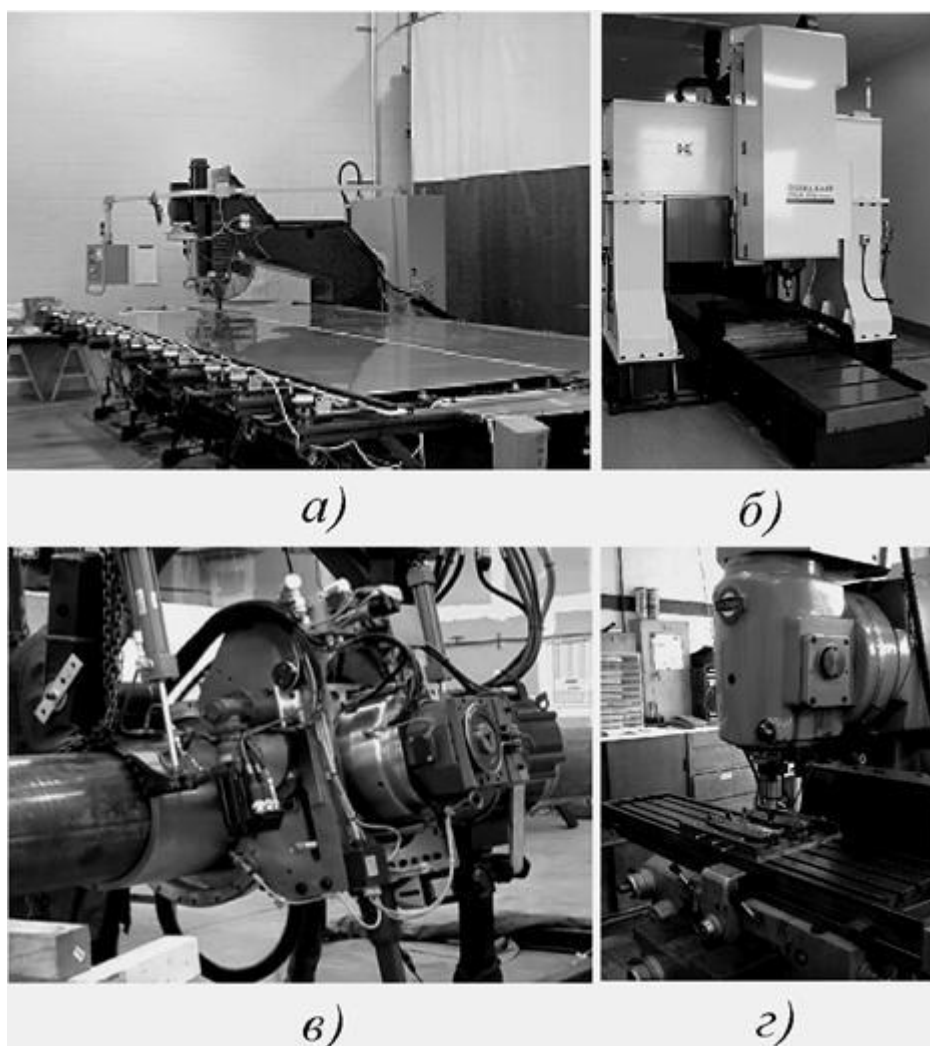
Оборудование для перемешивающей сварки трением: а – консольного типа; б – портального типа; в – устройство для сварки труб; г – установка на базе модернизированного фрезерного станка.
